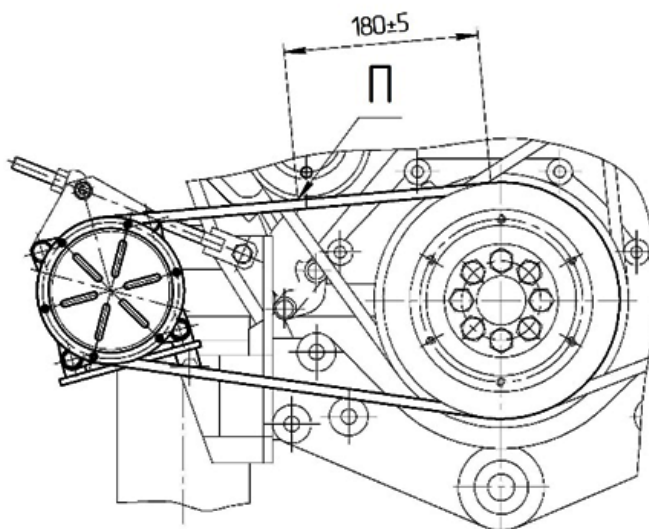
Регулировка ремня привода компрессора, установленного на двигателе
